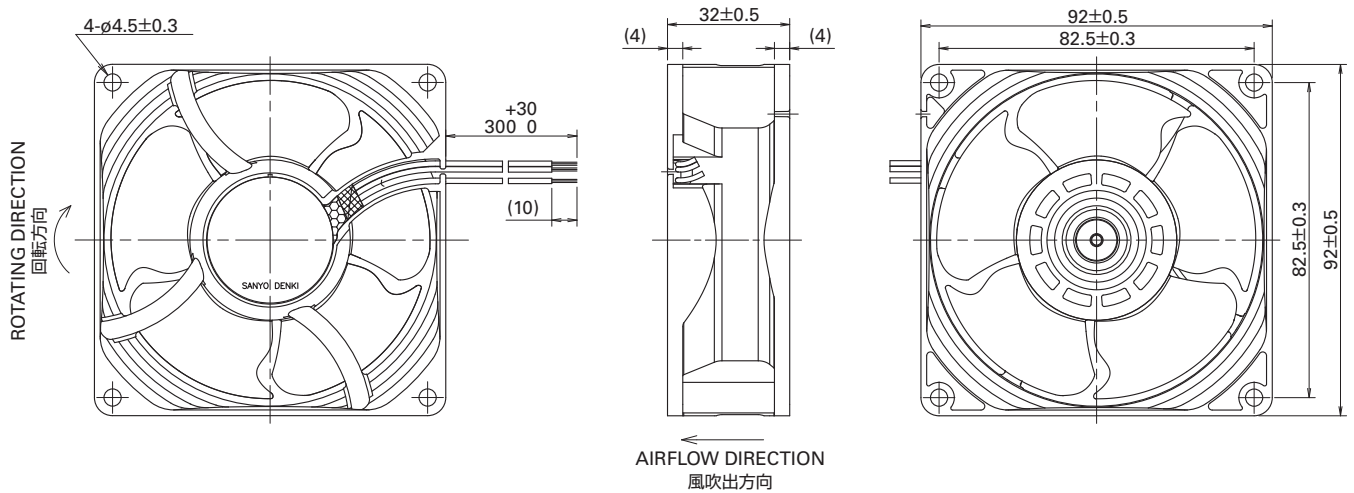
「San Ace 92WF」寸法緒元 (単位: mm)
